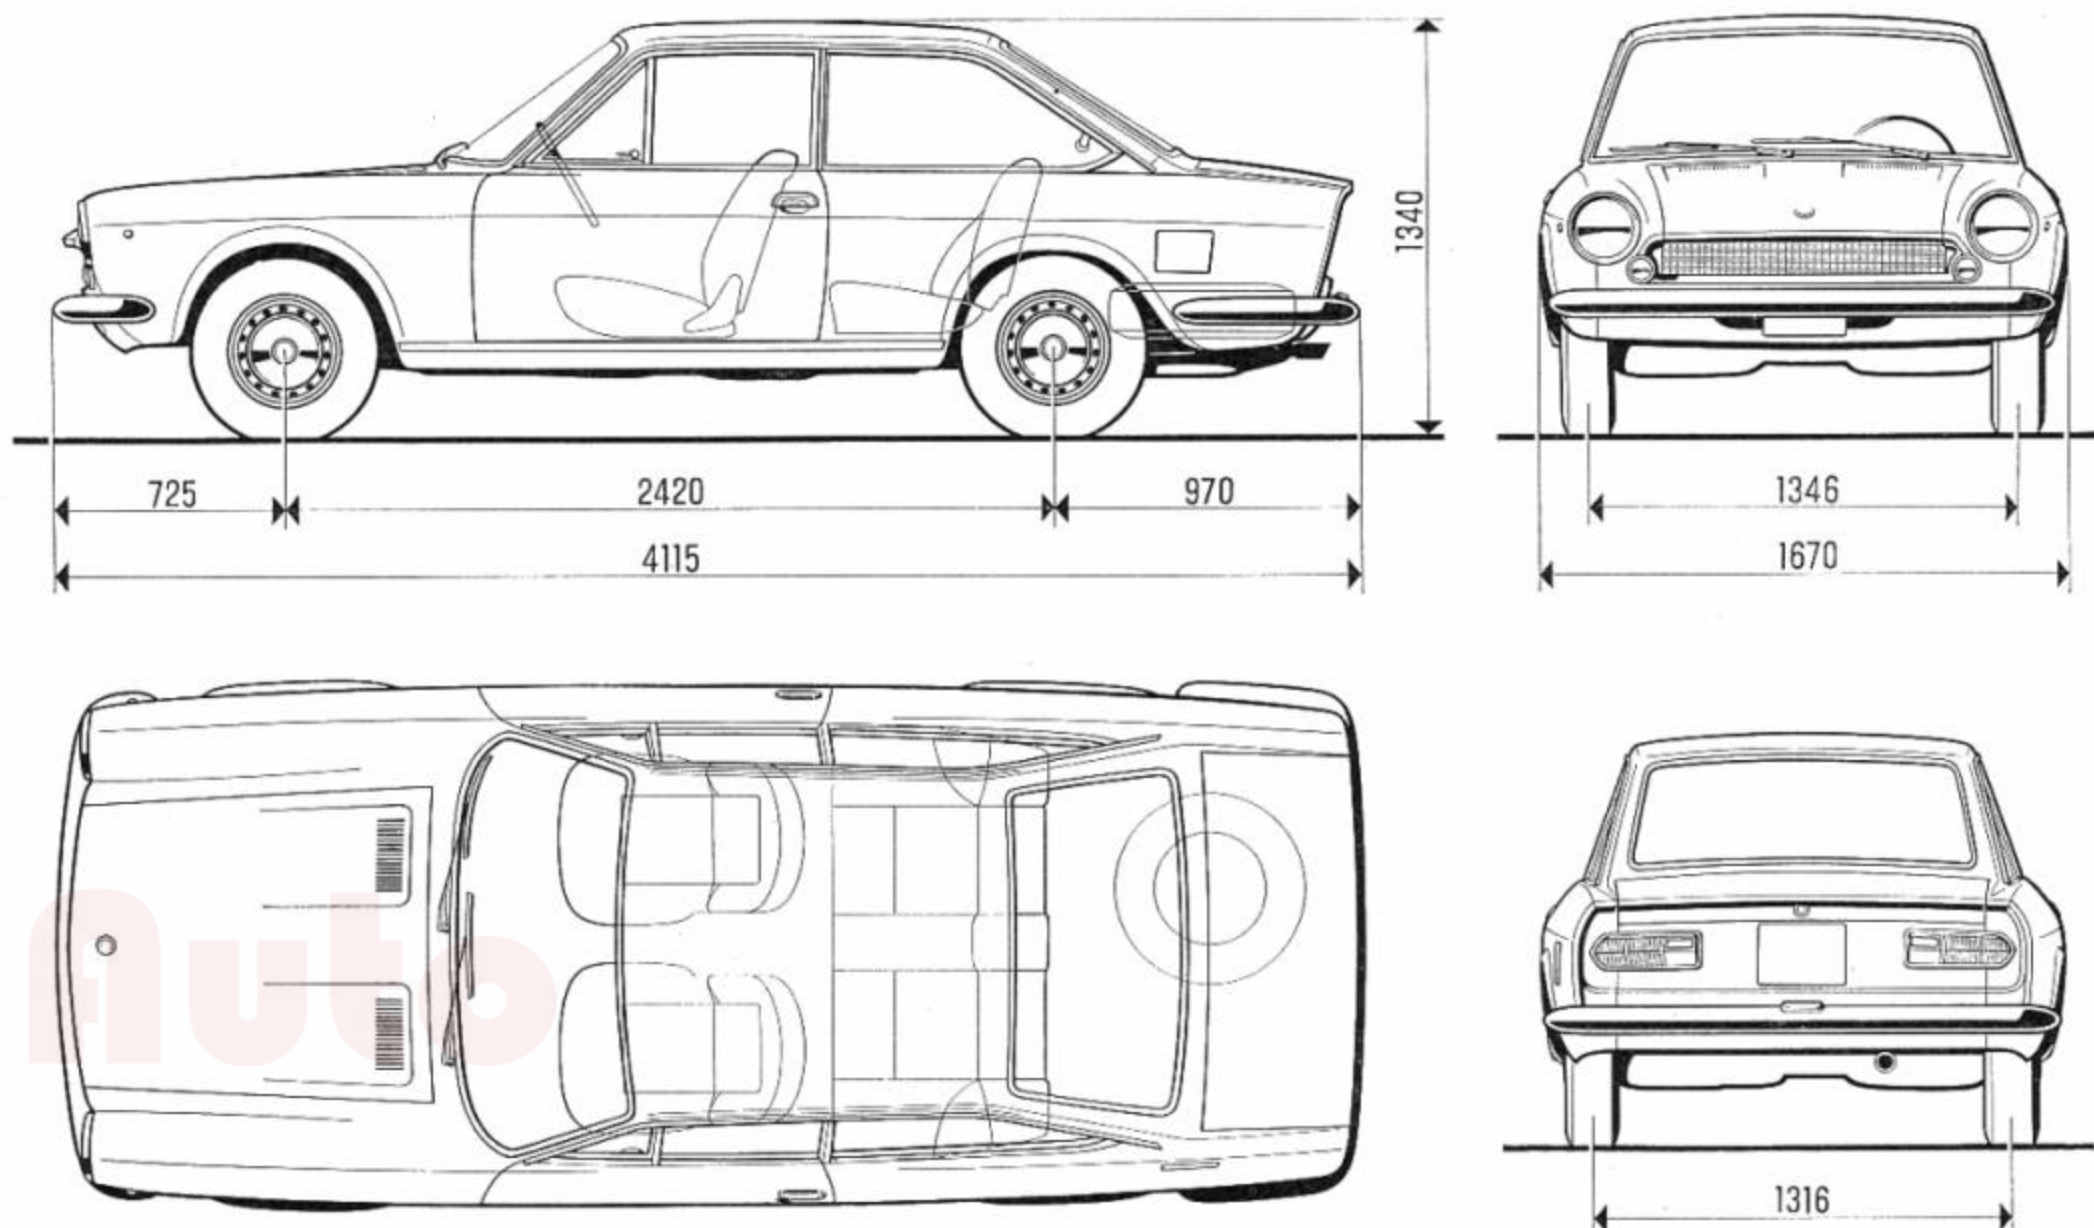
Hauptabmessungen des Fahrzeugs (die Höhe versteht sich bei unbelastetem Fahrzeug).
